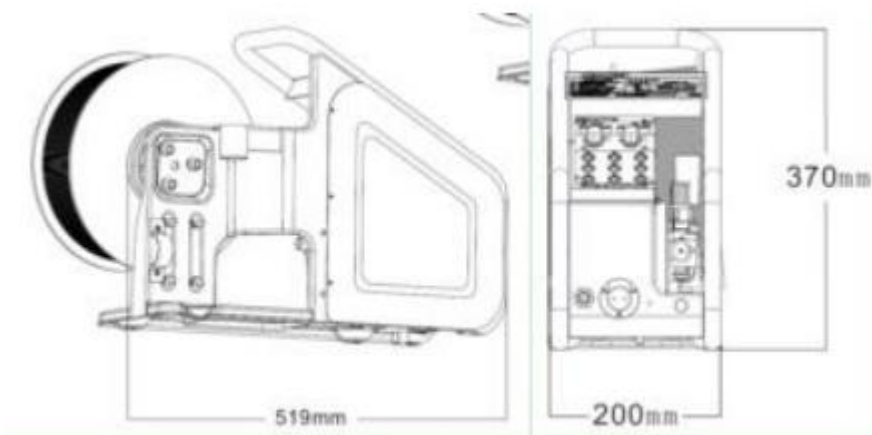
Габаритные размеры облегчённого блока подачи проволоки
